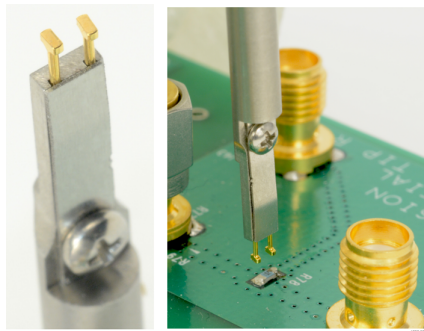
Utilizzo del supporto alla saldatura per installare i pin quadrati sul circuito stampato
